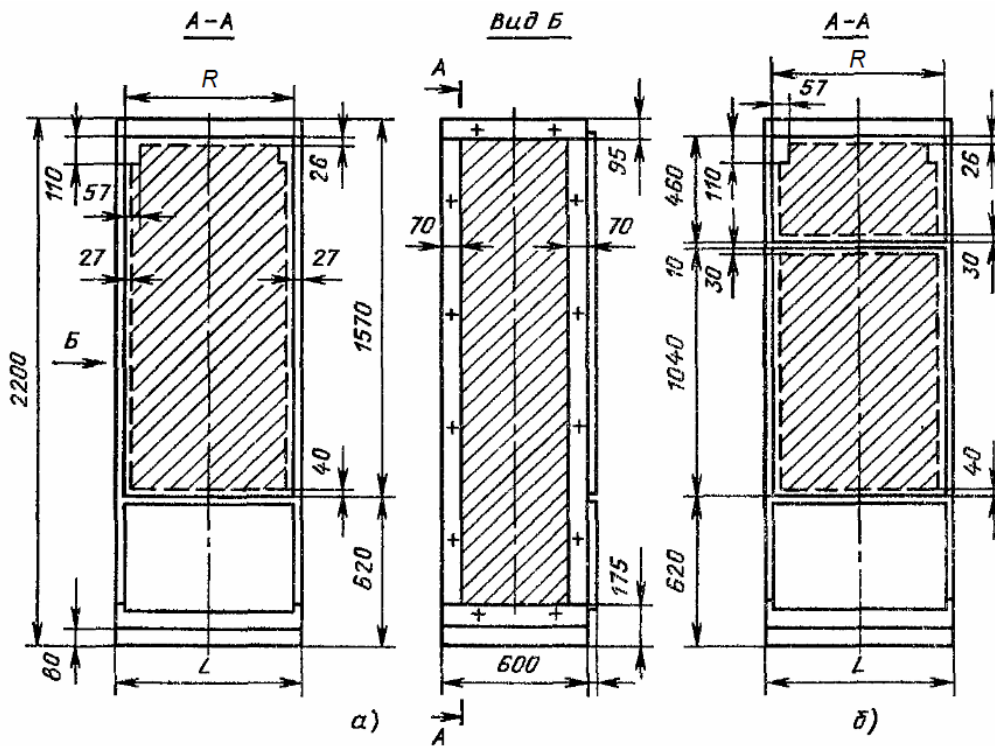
Монтажні зони панелі з каркасом щита ЦПК:
